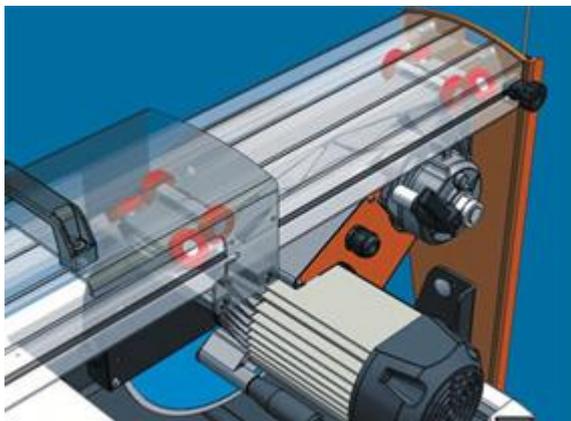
Салазки двигателя камнерезного станка PRIME.
